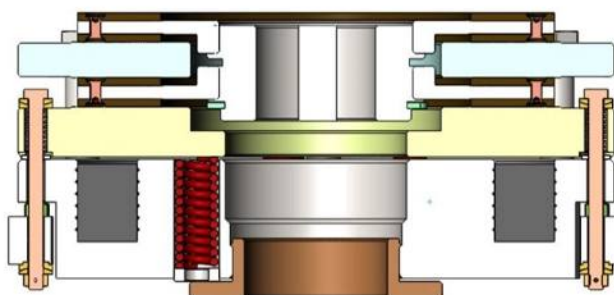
Тормозное устройство итальянской конструкции в разрезе
